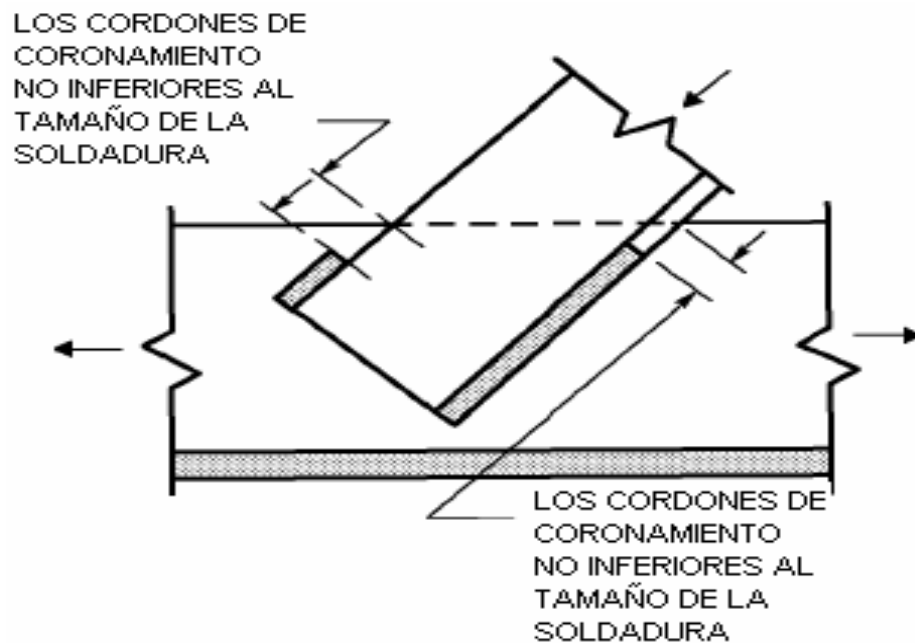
Terminaciones de las soldaduras de Filete
